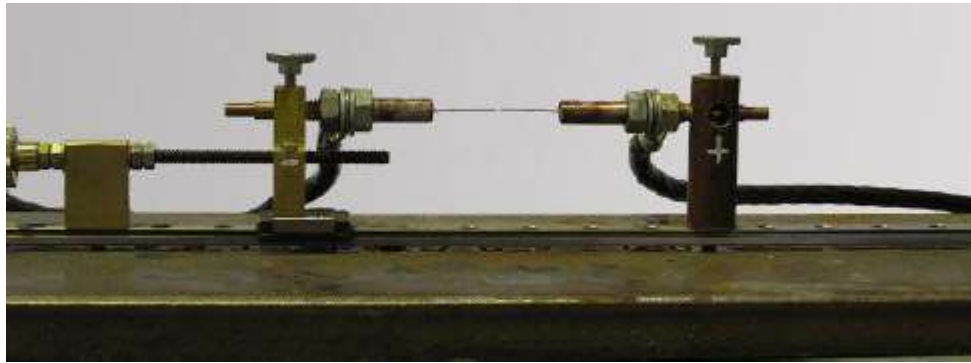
6 – Aparato utilizado para auxílio da soldagem de termopares. Fonte: KLUG, 2012.
